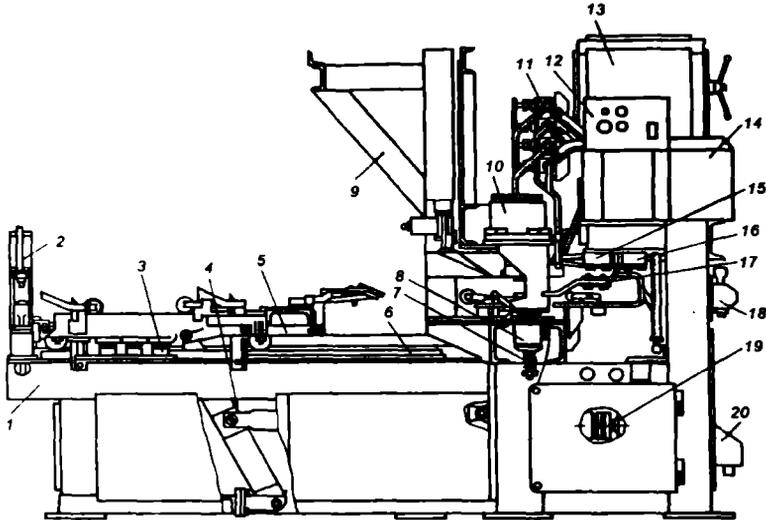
Схема сварочной машины МТМ-32УЖ14:
